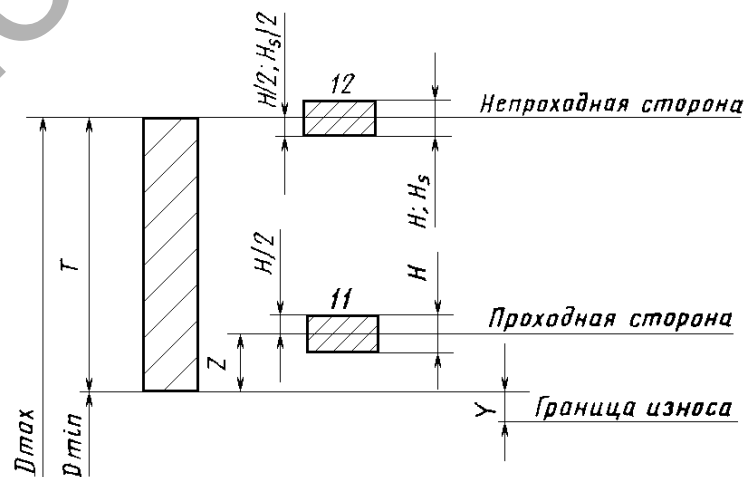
Схема расположения полей допусков калибров для отверстия
